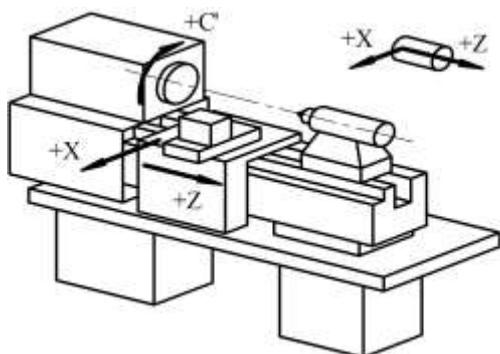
Обозначение осей и положительные направления движения токарно-винторезного станка
